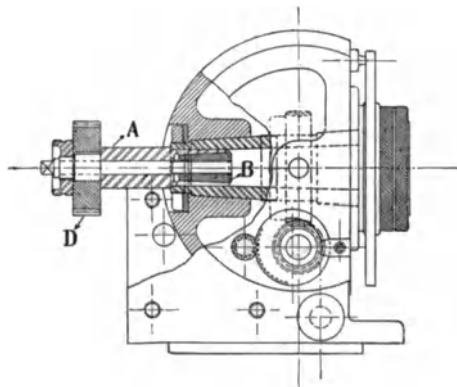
a. Die Befestigung des Wechselrades an der Hauptspindel.
